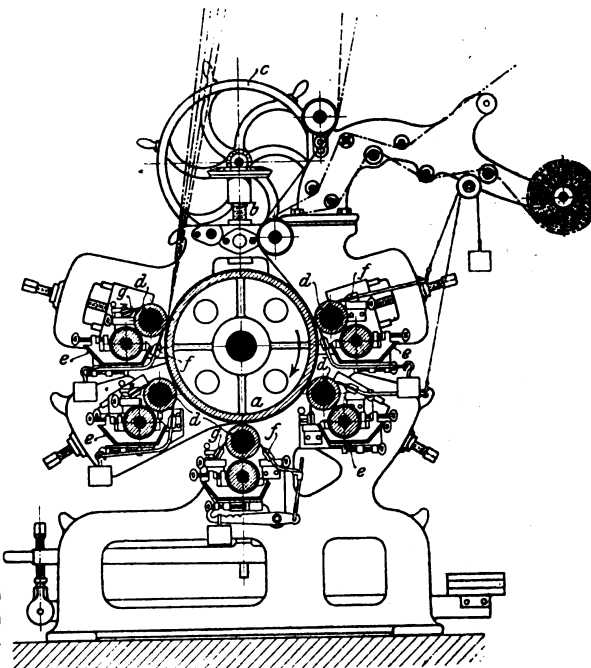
Walzen- oder Rouleauxdruckmaschine.
